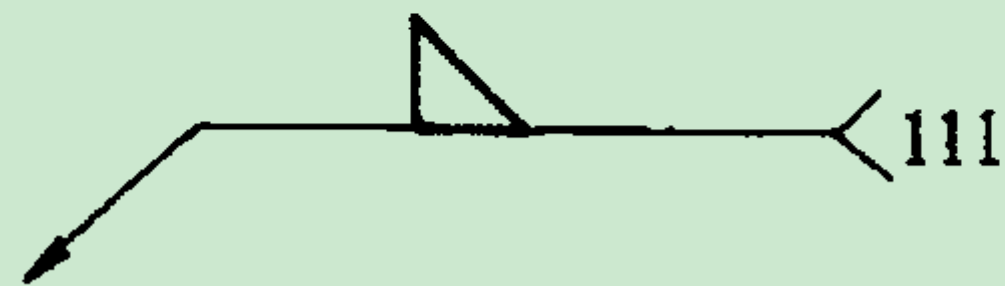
角焊缝采用焊条电弧焊
